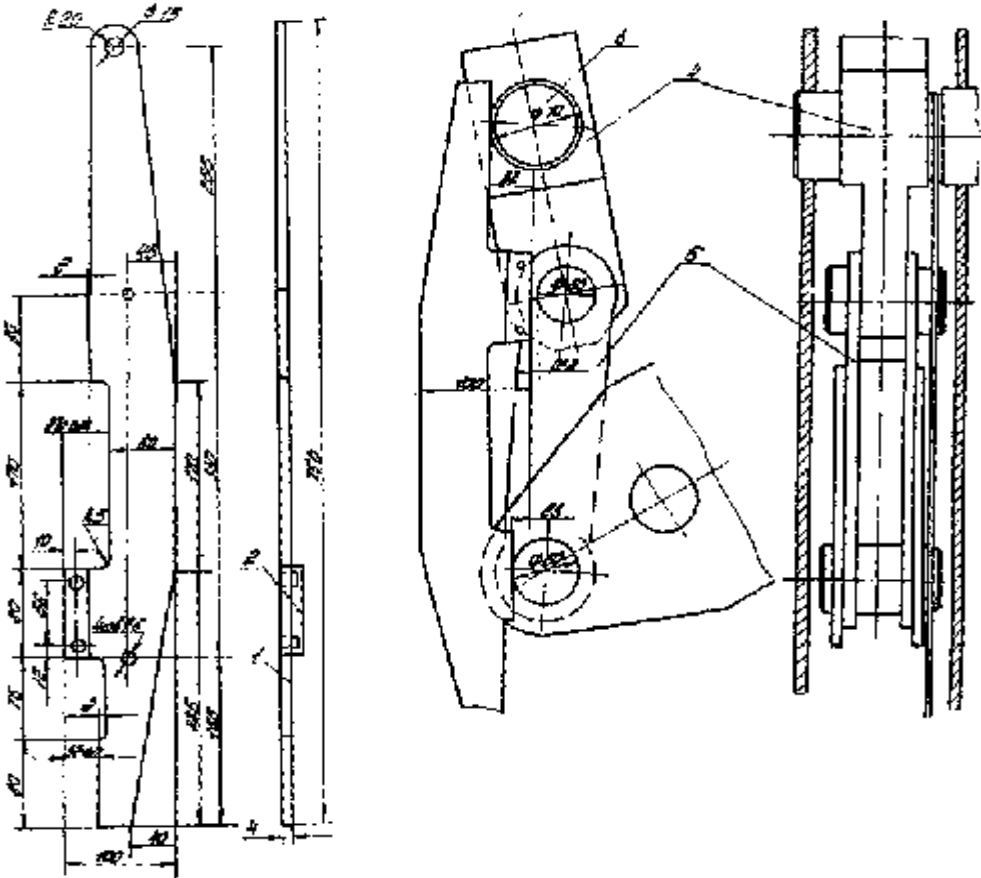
Шаблон для регулировки механизма выключателя в схема проверки шаблоном включенного положения рычагов механизма:
